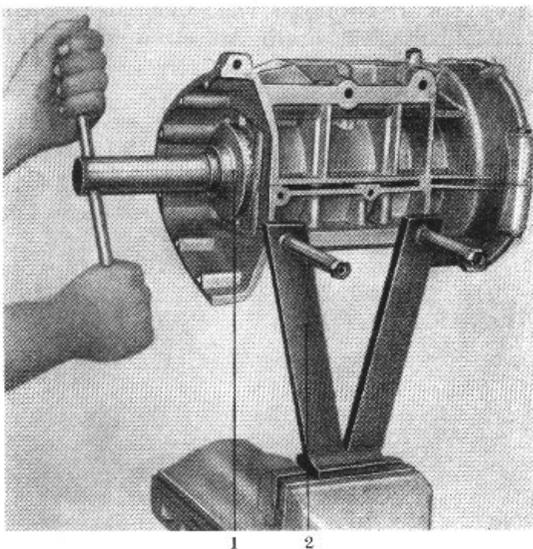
Planflächen für Lagerflansche nachfräsen
